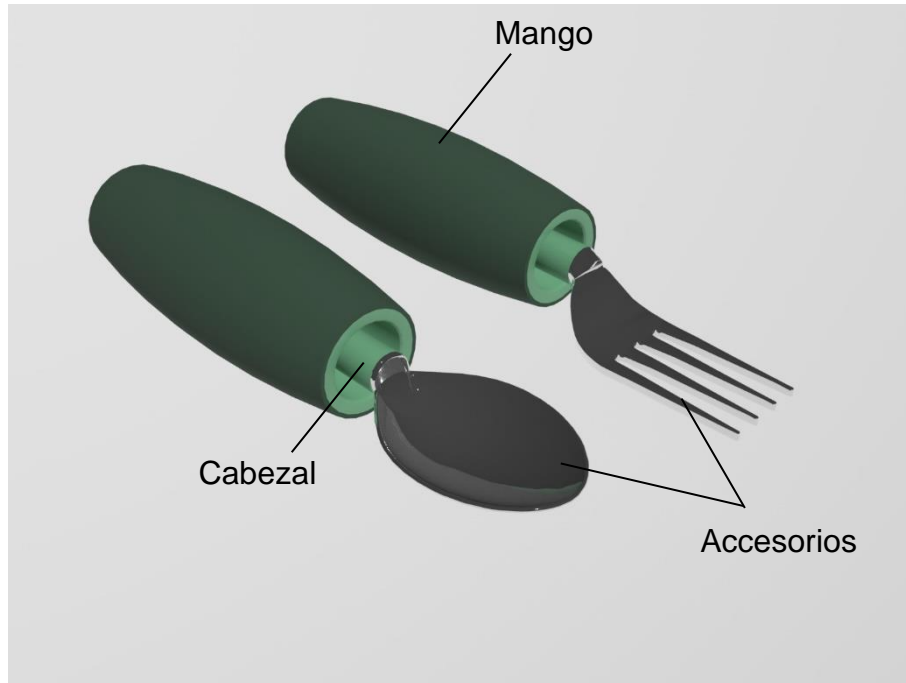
Montajes cubiertos. Fuente: elaboración propia
